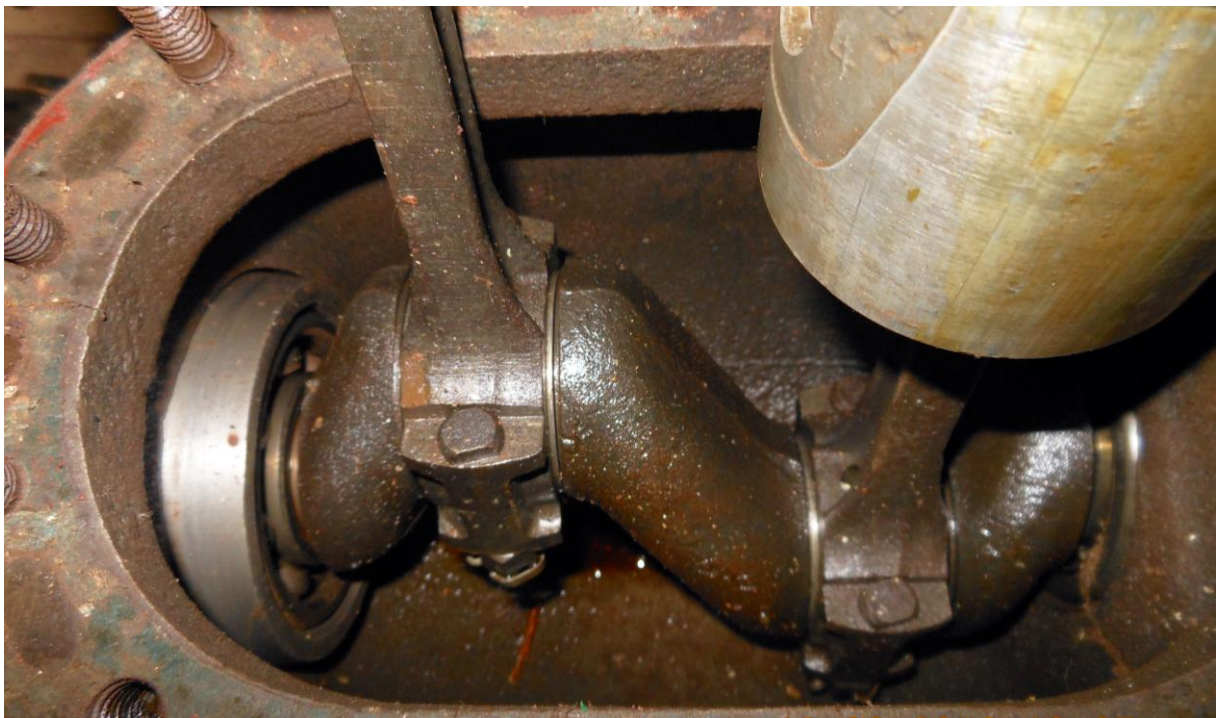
Внешний вид коленчатого вала и его опорных и шатунных подшипников
